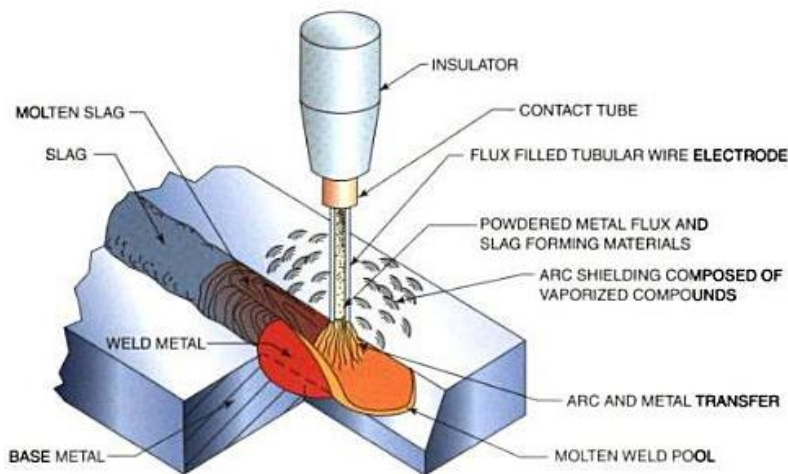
Soldadura FCAW auto protegida. (Jeffus, 2009)
